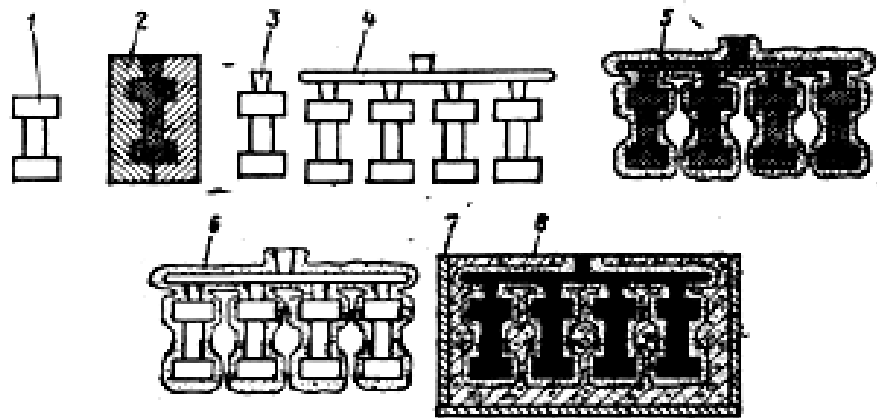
Технологическая последовательность процесса изготовления отливок по выплавляемым моделям: 1-деталь; 2-пресс-форма; 3-модель; 4-литейный блок; 5-огнеупорное покрытие; 6-керамическая оболочка; 7-опока; 8-опорный наполнитель.
